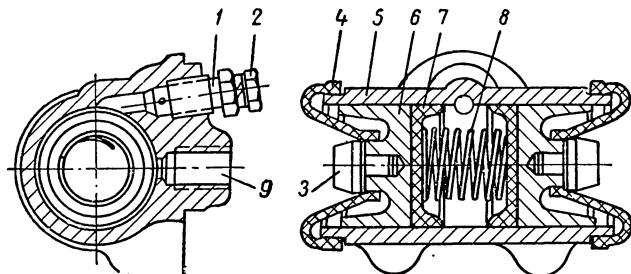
Главный цилиндр гидравлического привода тормозов:
